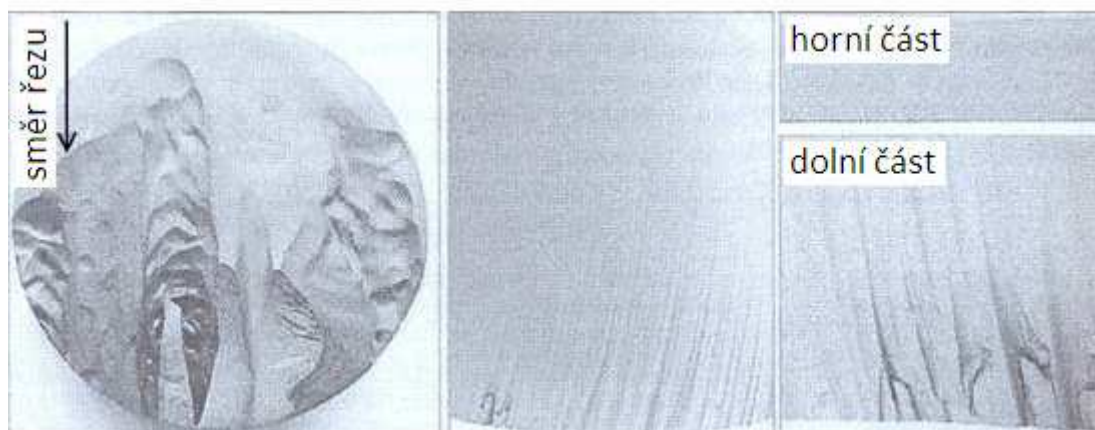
Zvednutá hrana po řezání AWJ (5)
